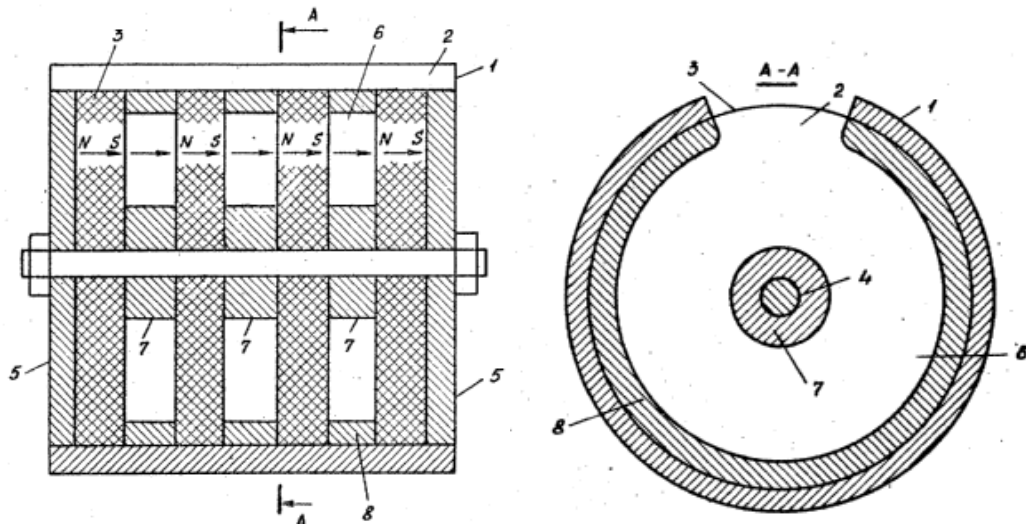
Пристрій для передпосівної обробки насіння з постійними дисковими магнітами
